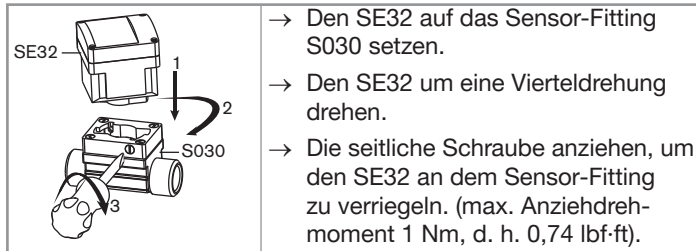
Montage des SE32 auf das Sensor-Fitting S030
